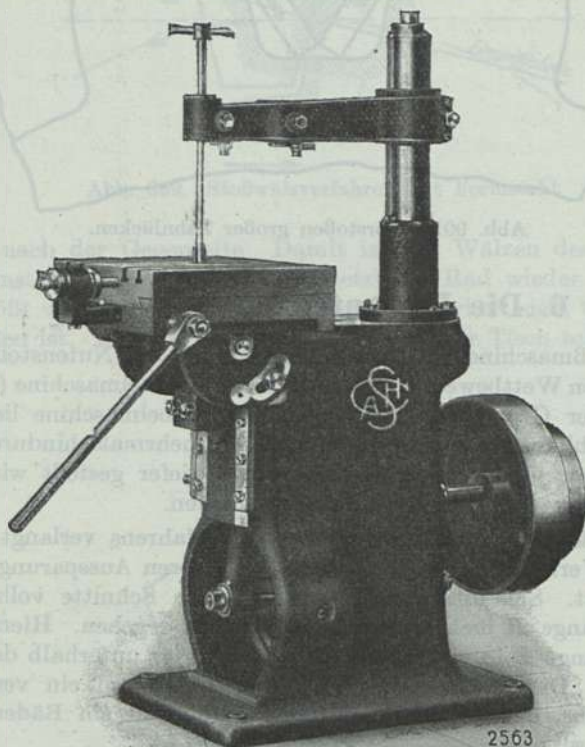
Keilnutenhobelmaschine. A. H. Schütte, Köln-Deutz.
